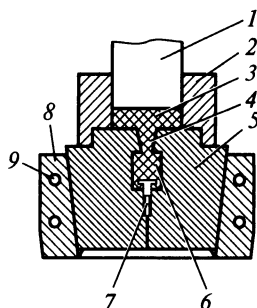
Рабочая часть пресс-формы для литьевого прессования с верхней камерой прессования:
